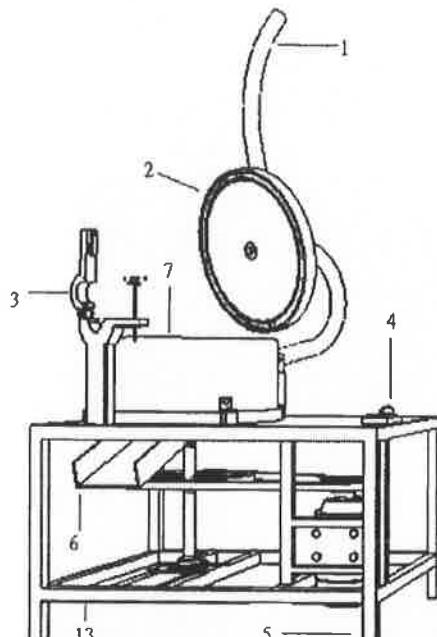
แบบเครื่องแยกผลปาล์มจากทะลายปาล์มน้ำมัน
